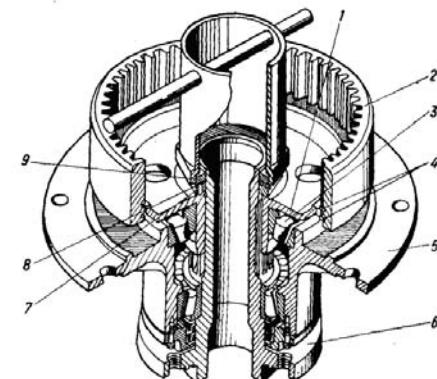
Снятие эпicyклического зубчатого колеса, корпуса: 1 — ступица; 2 — колесо зубчатое; 3 — подшипник; 4 — кольцо стопорное; 5 — картер; 6 — ступица редукторная; 7 — гайка; 8 — шайба; 9 — контргайка
